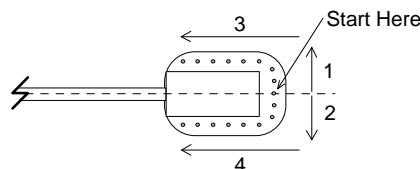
Secuencia del Soldado por Puntos - Filas Exteriores
